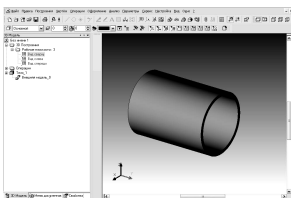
Твёрдотельная модель корпуса в T-FLEX CAD 11
